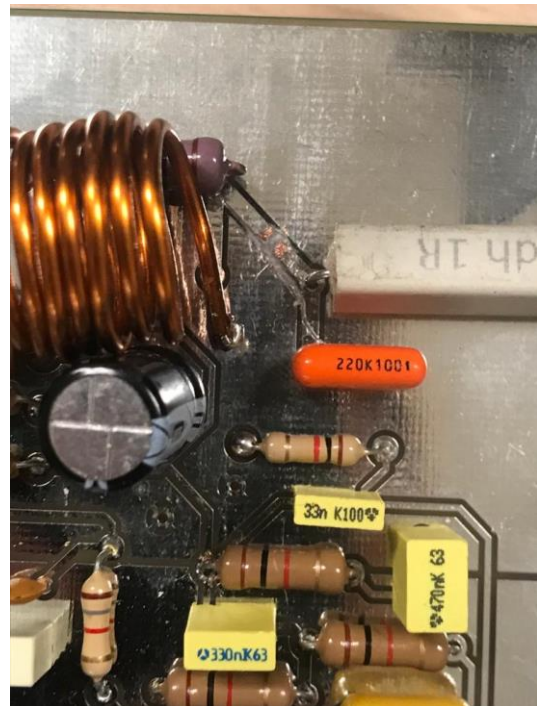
Part superior PCB, on es veu l'extracció de coure.
